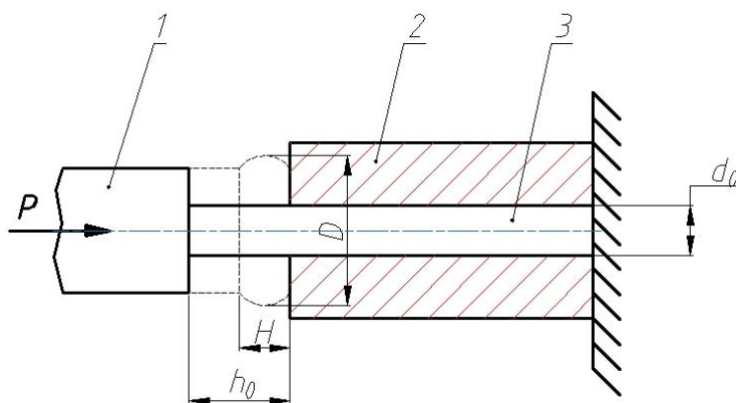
Схема процесу висадки: 1 – пуансон; 2 – матриця; 3 – заготовка.
